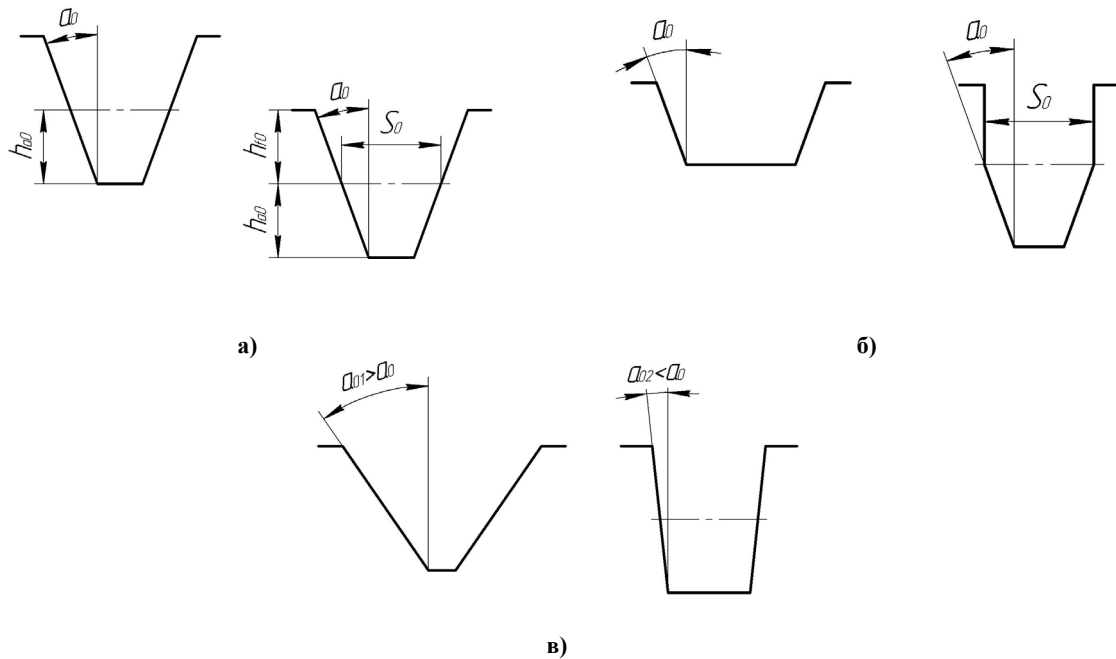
Схеми двох прохідного оброблення зубчастих коліс.
